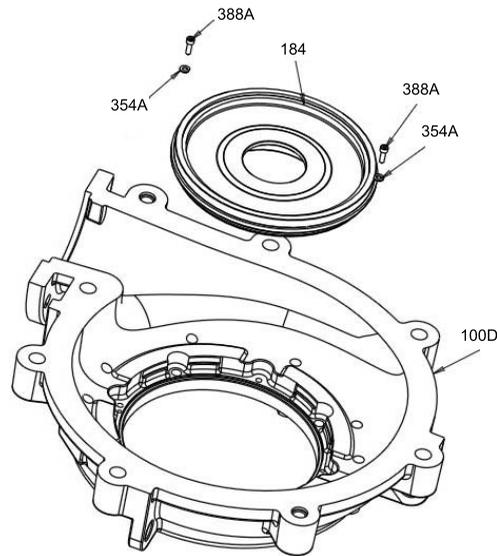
Installation du demi-corps de presse-étoupe et du couvercle d'étanchéité
